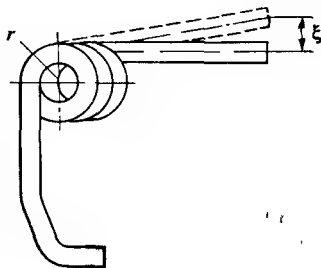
Вид многовитковой пружины показывающего манометра
